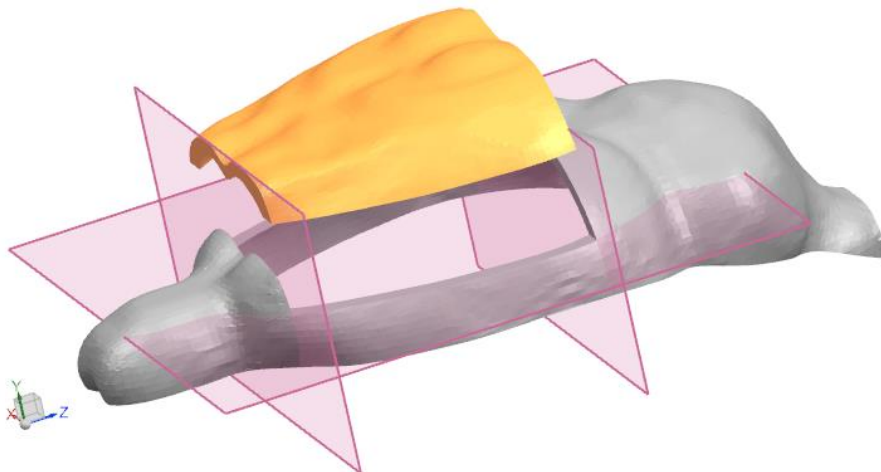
Extracción de la Tapa (Pieza 12) a partir de la Carcasa Superior (Pieza 11).
